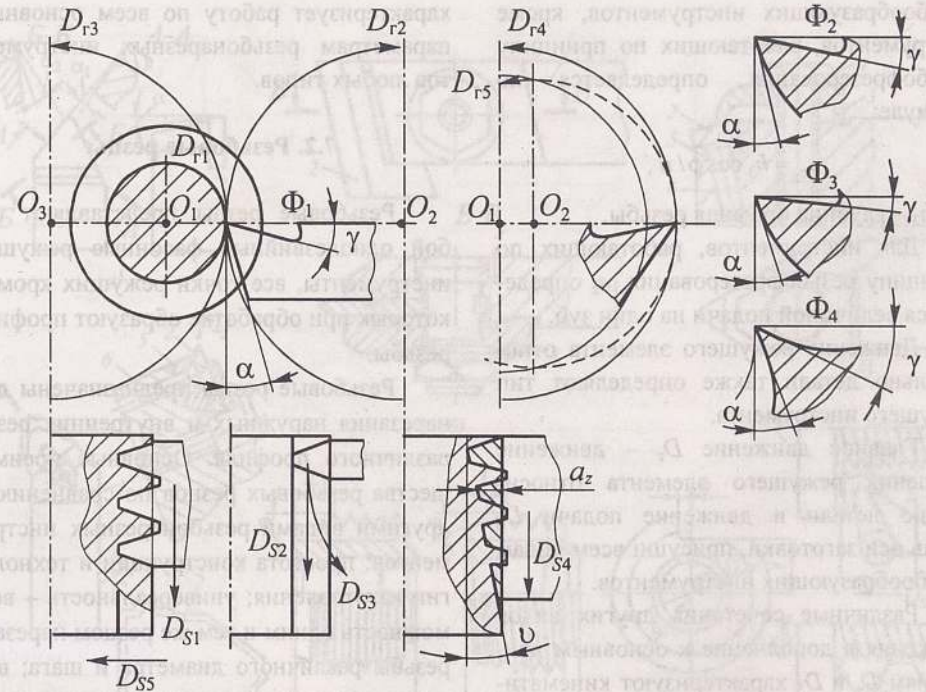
Обобщенная модель образования резьбы резьбонарезными инструментами
